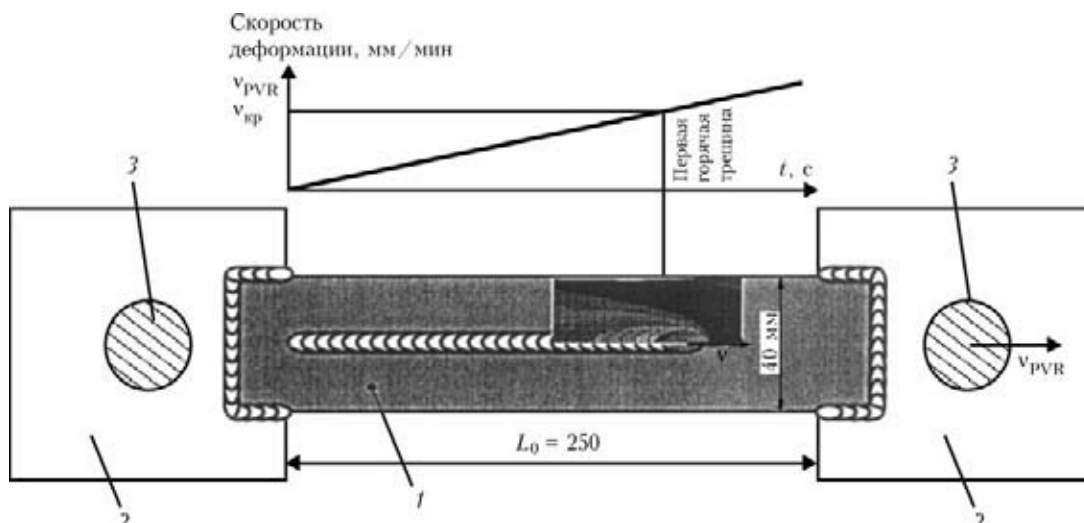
Схема принципа реализации PVR-Test [11]: 1 — образец; 2 — захваты; 3 — крепежные штифты для нагружения образцов
